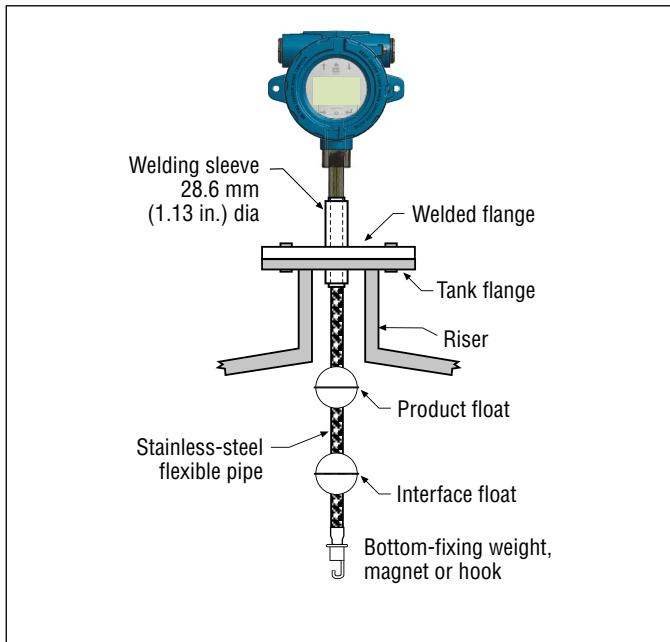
Montagem em flange soldado para haste flexível
